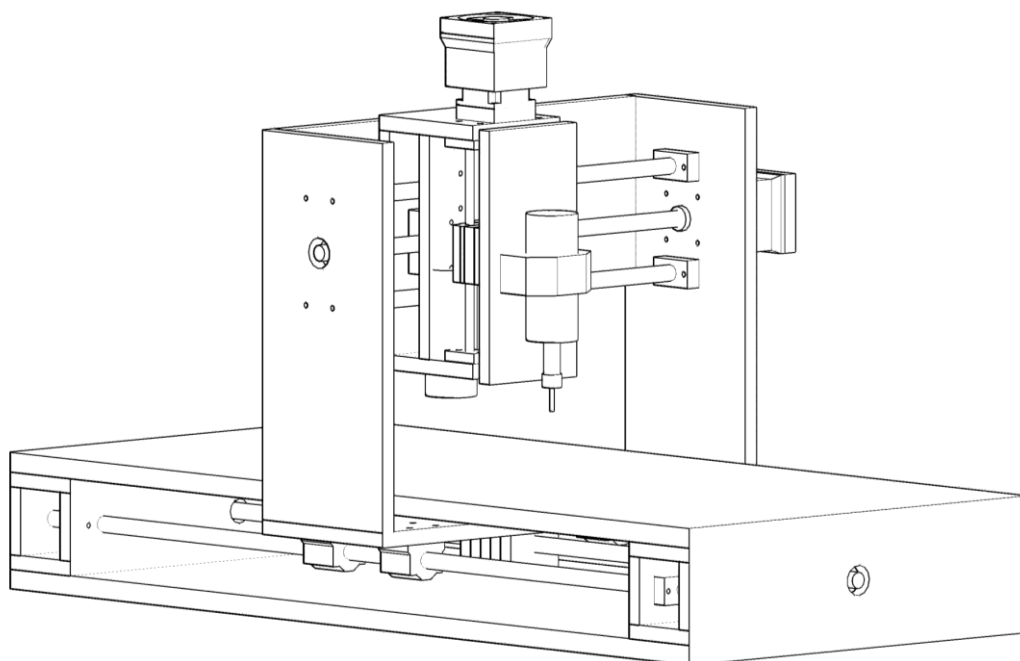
Конструктив верстата з ЧПУ вид зліва
